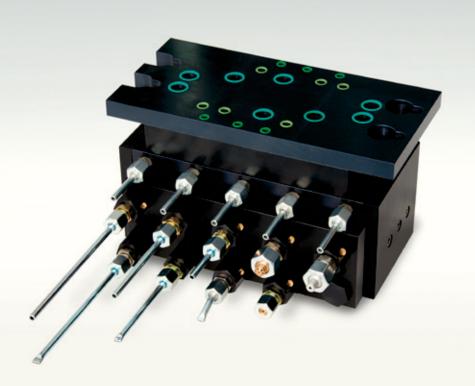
Kreis Sprüh- und Blaswerkzeug
